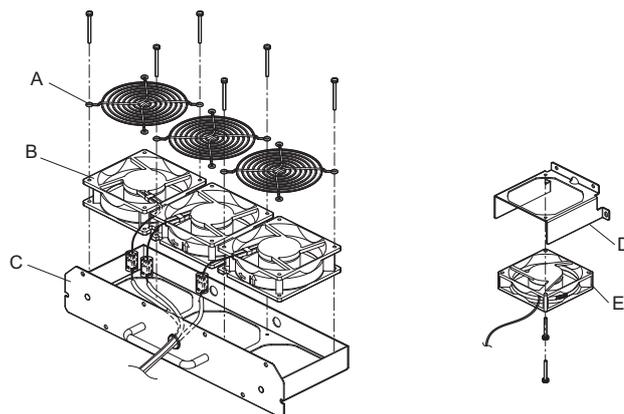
Демонтаж вентиляторных модулей: 4A0414
